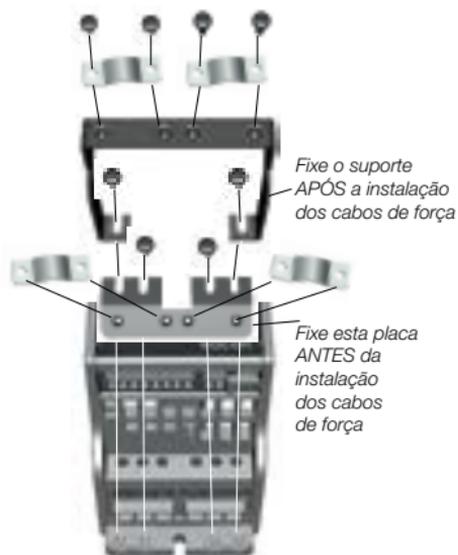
Montagem da placa PE e suporte a cabo API, MI1 - MI3
